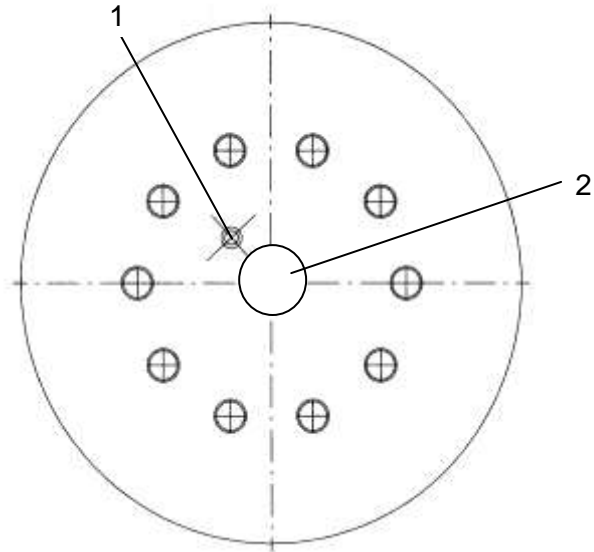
Крышка-анод с расположением цилиндрических заготовок имплантатов (вид снизу)
